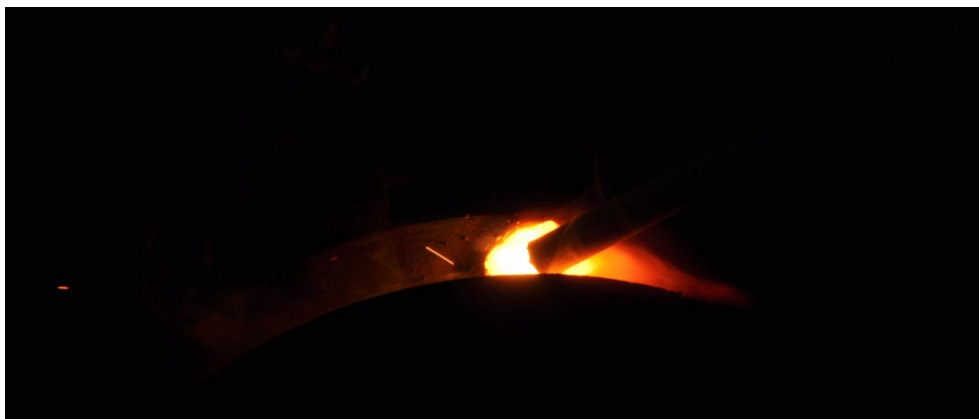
Zplodiny vznikající hořením obalu elektrody
